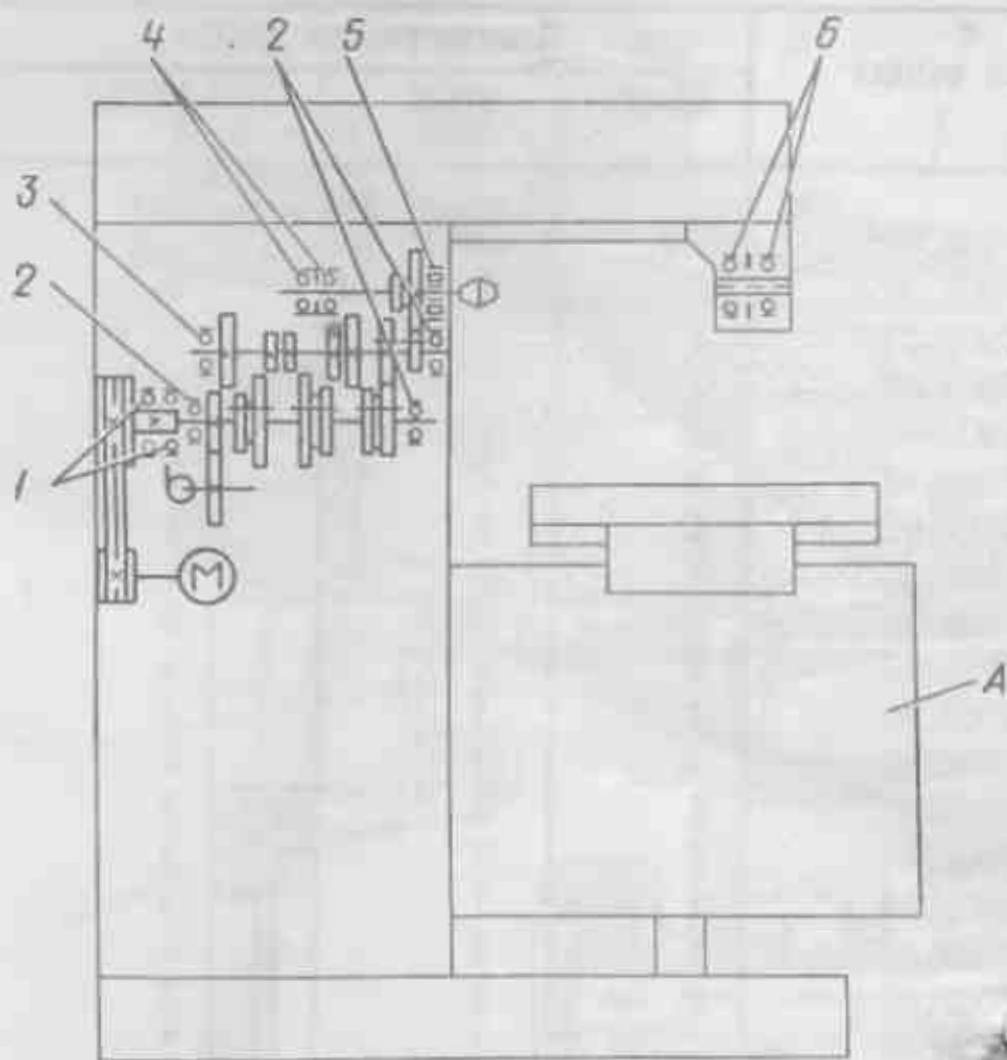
Схема расположения подшипников станков 6T80Г и 6T80
